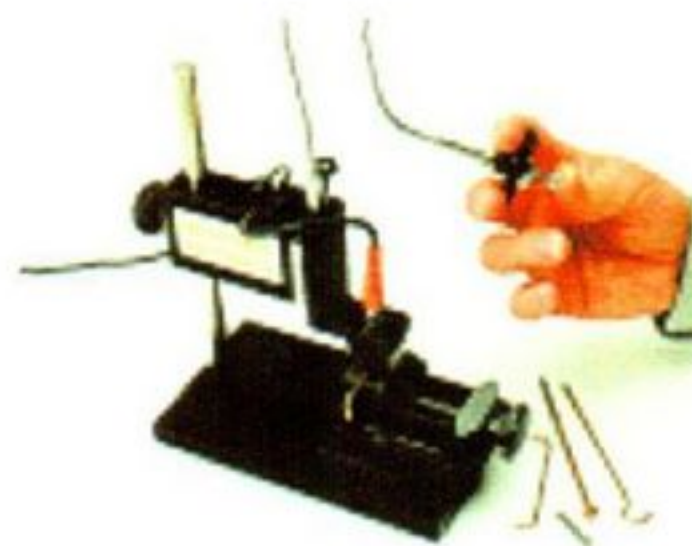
Приспособление для позиционирования преобразователей и деталей
